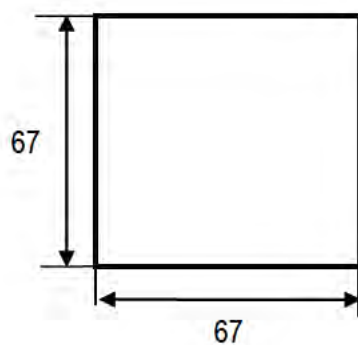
Разметка щита для крепления ИП для конструктивного исполнения М
